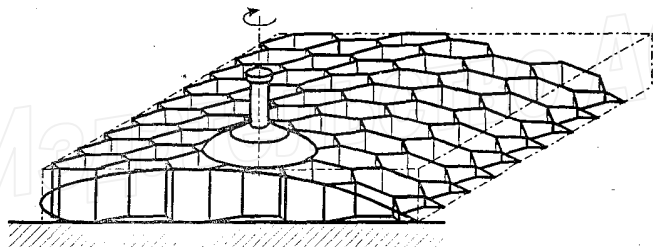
Получение сотоблока переменной высоты фрезерованием
